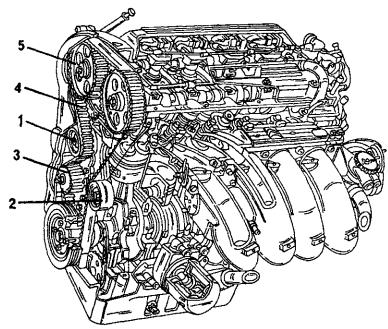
Привод газораспределительного механизма 16-клапанного двигателя.
